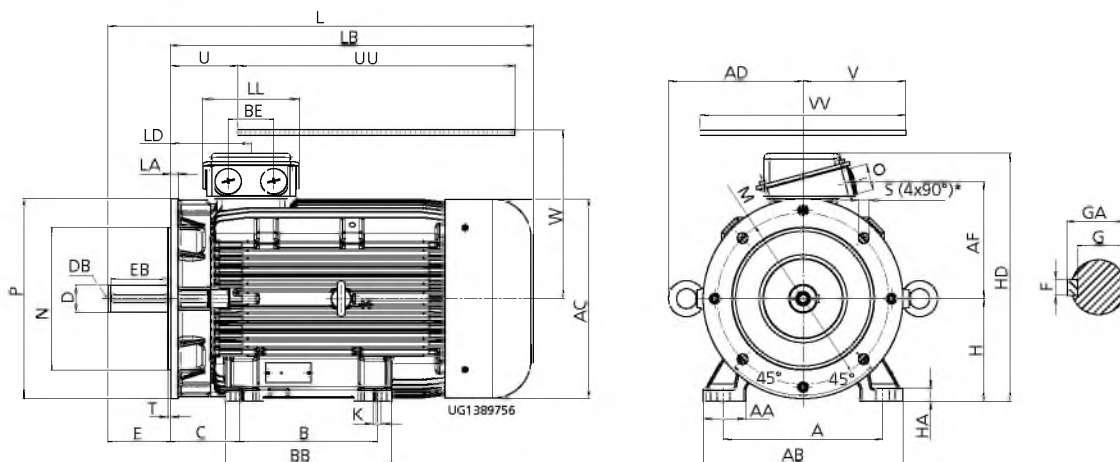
Двигатель с клеммной коробкой и фланцем FF с проходными отверстиями (V15,...)
